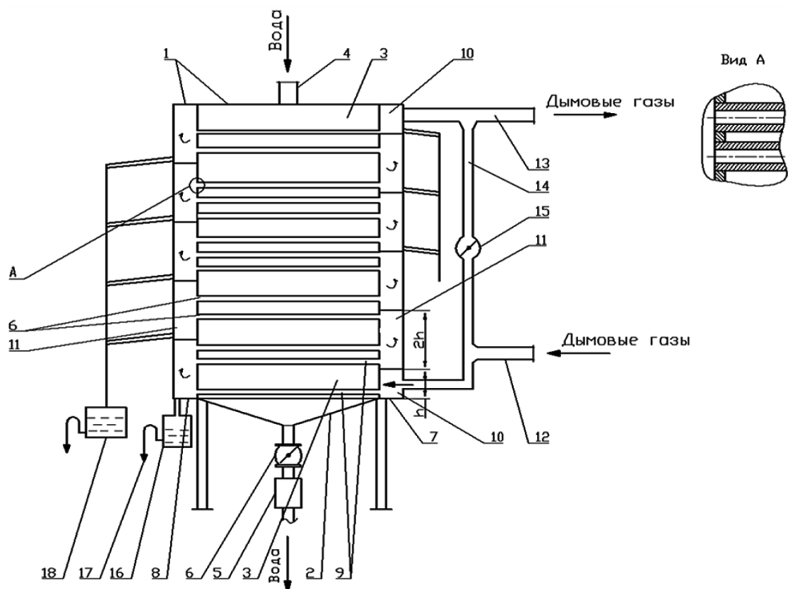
Схема теплоутилизатора (вид А – соединение труб с рубашками): 1 – корпус; 2 – основание; 3 – изолированный резервуар; 4 – патрубок для подачи воды; 5 – насос; 6 – шибер; 7, 8 – рубашки; 9 – пучок труб; 10 – нижняя одинарная секция; 11 – двойная секция; 12, 13 – входной и выходной патрубок для дымовых газов; 14 – газоход; 15 – заслонка (шибер)
